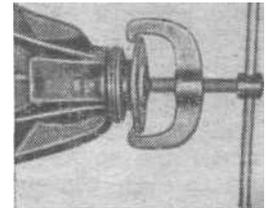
Съемник фланца вала ведущей шестерни редуктора
